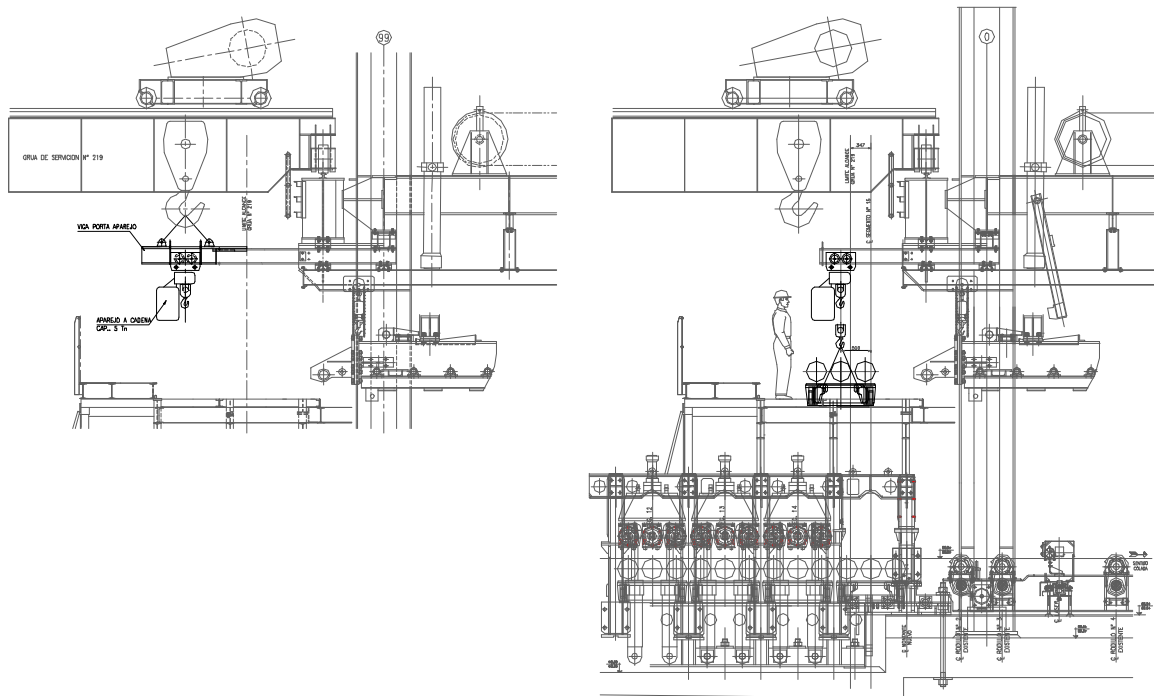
= Foto 7 – Montaje aparejo a cadena Fig. 8 = Foto 8 – Montaje segmento 15
